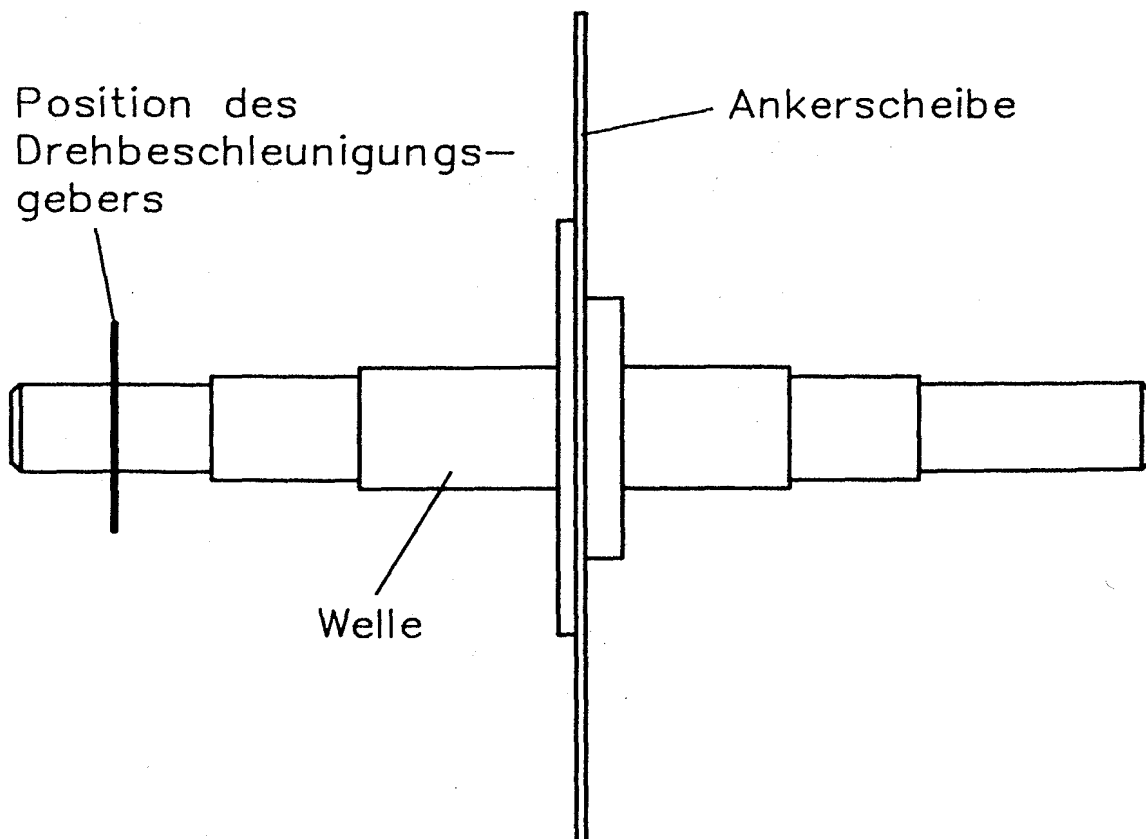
Mechanische Gestalt des Rotors der Gleichstrom-Scheibenläufermaschine und ausgeführte Positionierung des Drehbeschleunigungsgebers auf deren Welle.
